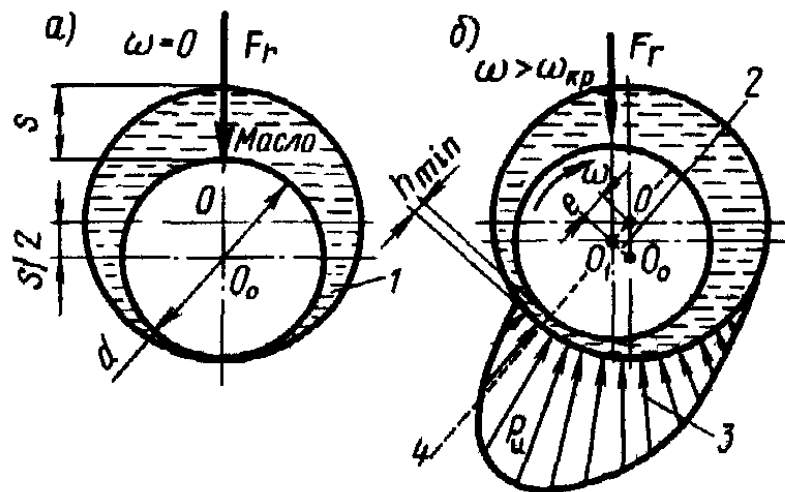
Гидродинамическая смазка подшипника скольжения
